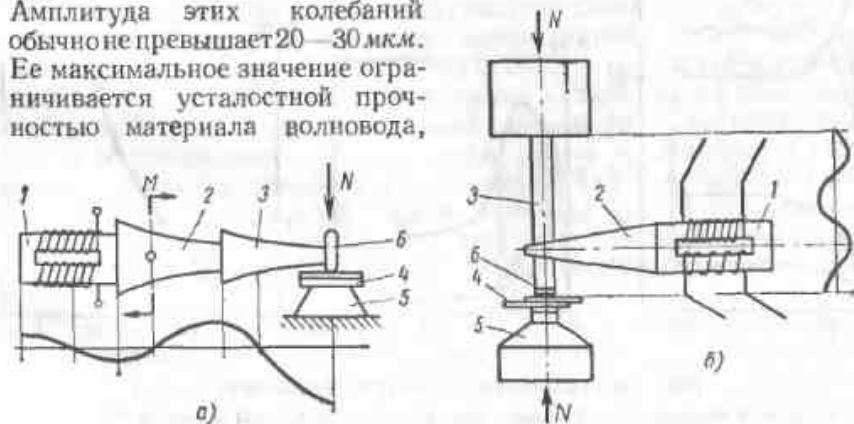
Схемы ультразвуковой сварки металлов:
